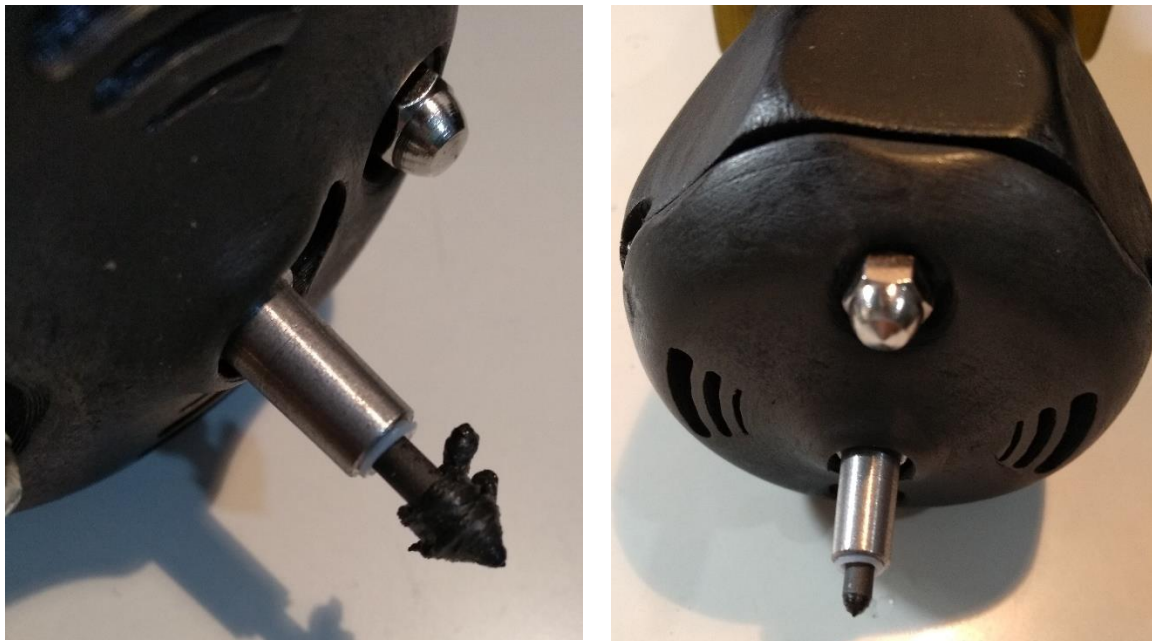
Forma de la herramienta para diferentes parámetros de soldadura. (Izquierda) Velocidad de giro de $4500 \text{ rpm} \pm 200 \text{ rpm}$. (Derecha) $2000 \text{ rpm} \pm 200 \text{ rpm}$. En ambos casos se usa filamento de PLA.
